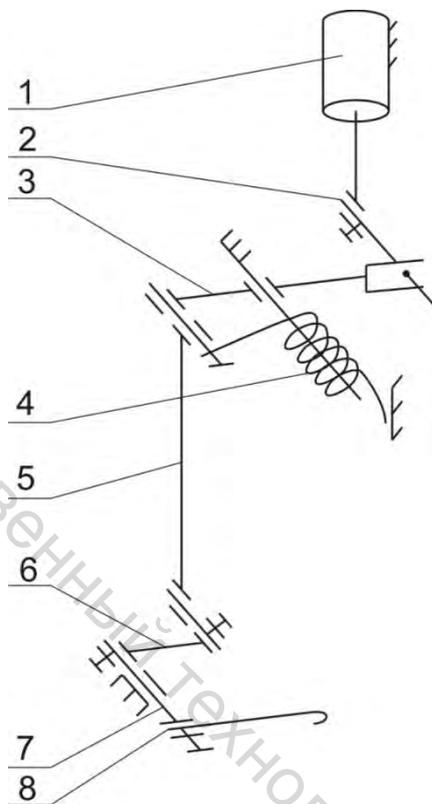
Кинематическая схема механизма нитеотводчика
